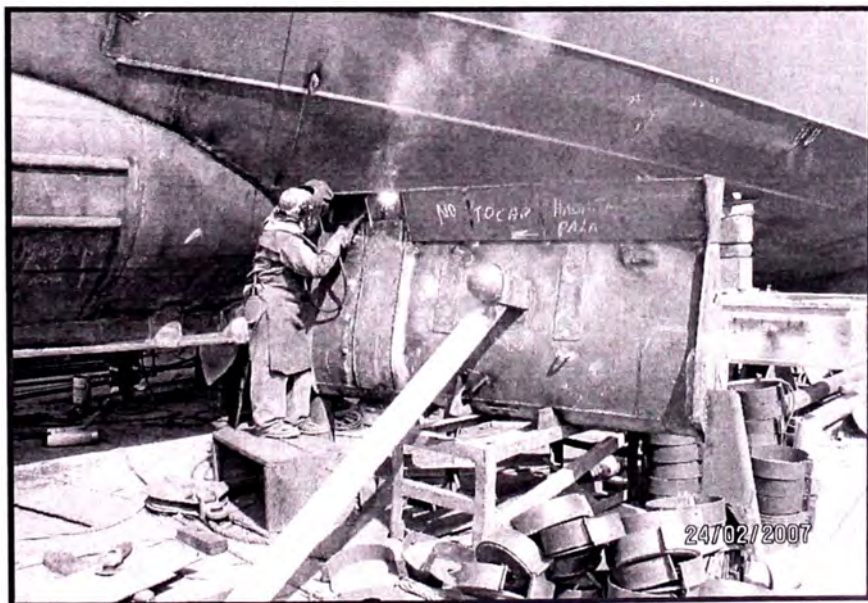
Vista del proceso de soldadura de la pala timón modificada.
